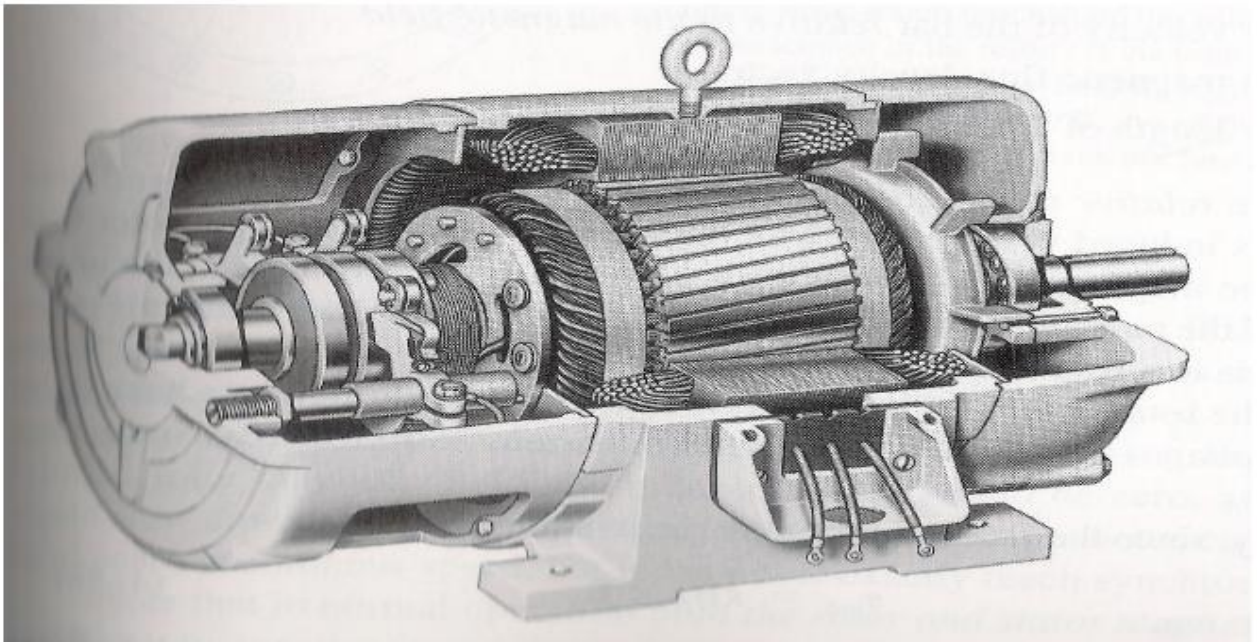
Coupe d'une machine asynchrone à rotor bobiné (standard) [13].
